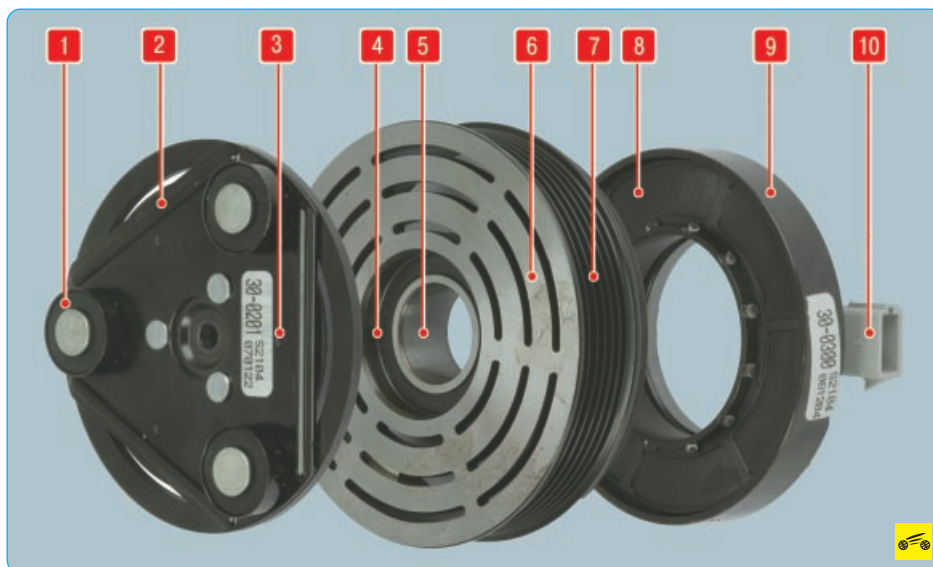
Электромагнитная муфта привода компрессора: 1 – упругий элемент диска; 2 – прижимной диск муфты; 3 – ведомый диск муфты; 4 – подшипник; 5 – внутренняя обойма подшипника; 6 – рабочая поверхность шкива; 7 – ручки шкива; 8 – обмотка электромагнита; 9 – корпус электромагнита; 10 – колодка электрического разъема
